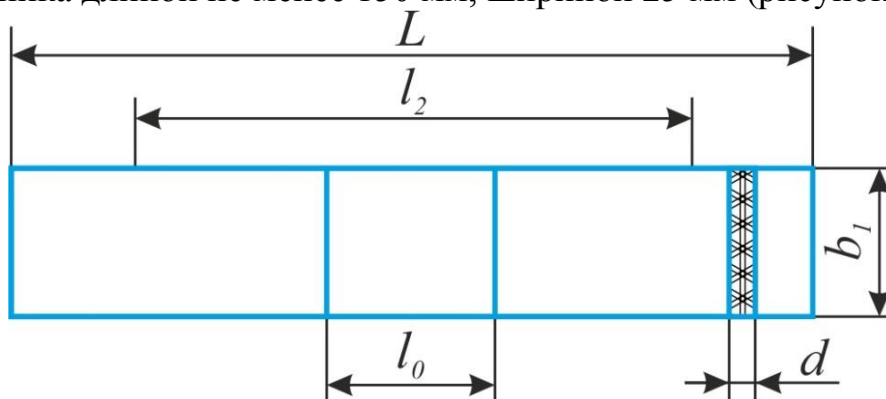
Размеры образца для полиэтиленовой пленки
